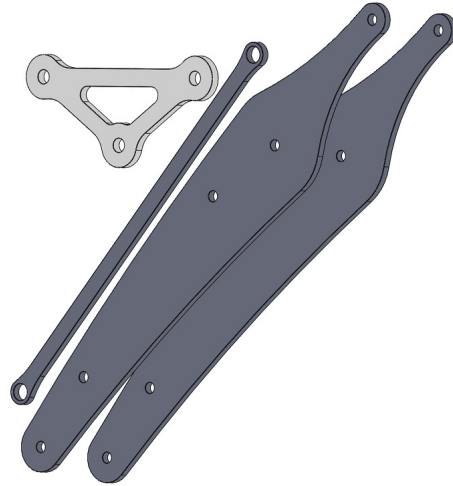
Vista explosionada del segundo eslabón del robot manipulador.
